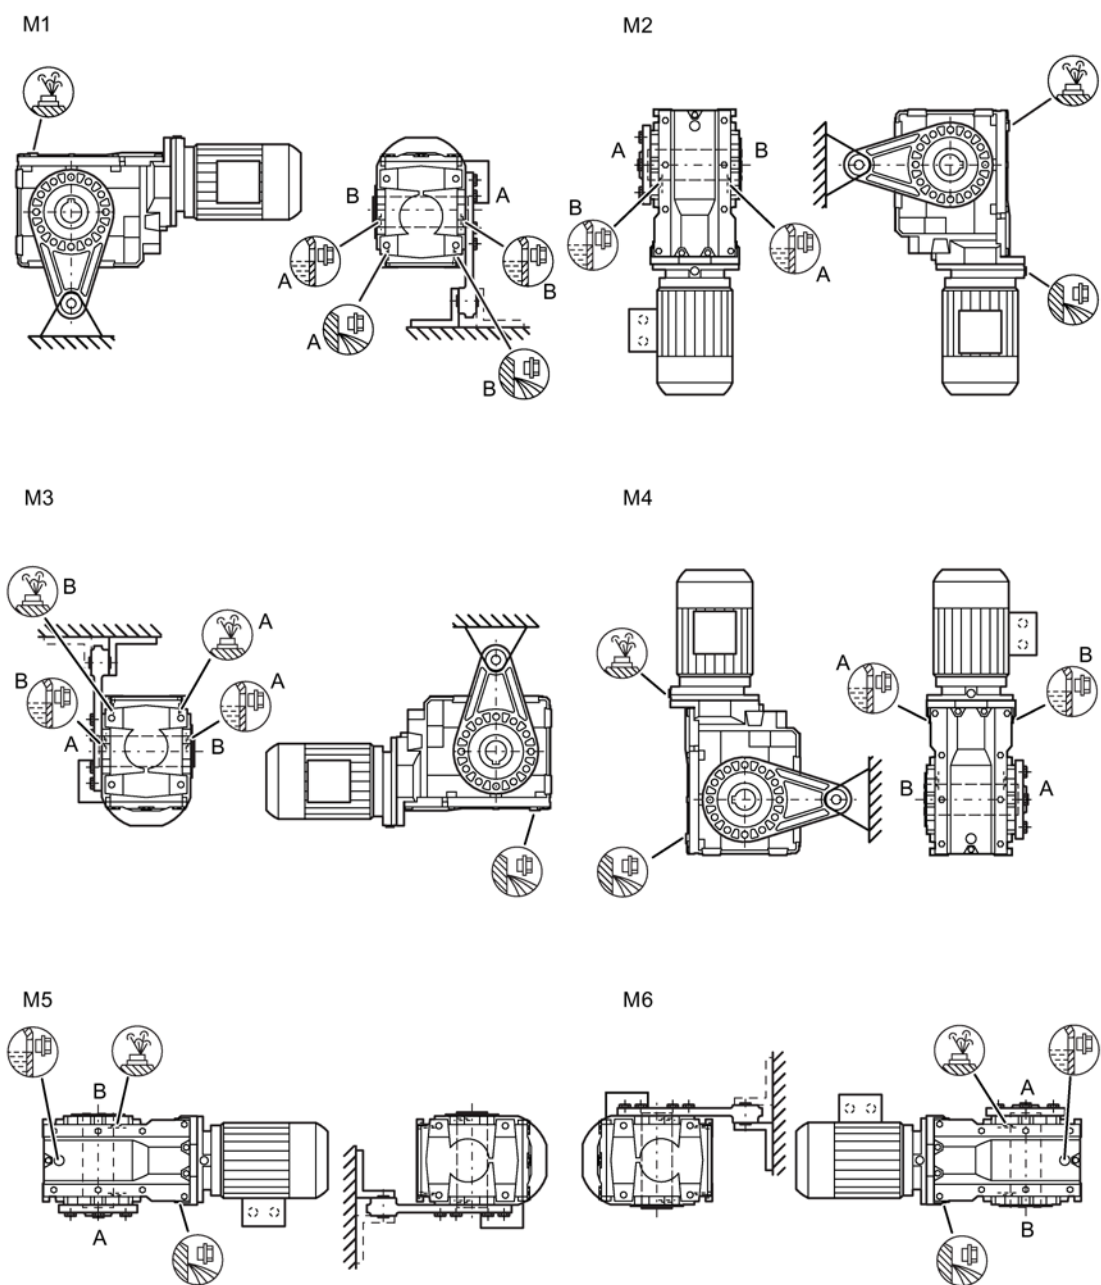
Монтажные положения для конического редуктора BAD в насадном исполнении, типоразмеры 39–49
